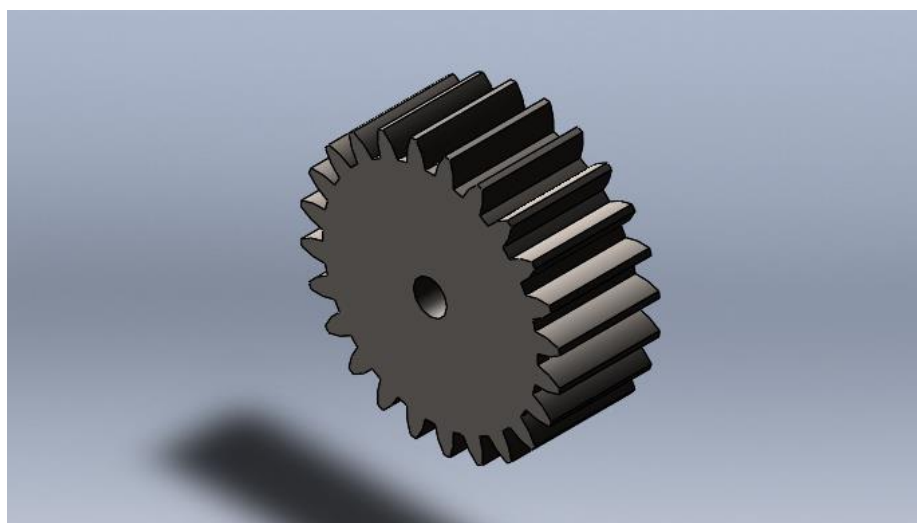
Кінцевий вигляд прямозубого циліндричного зубчастого колеса
